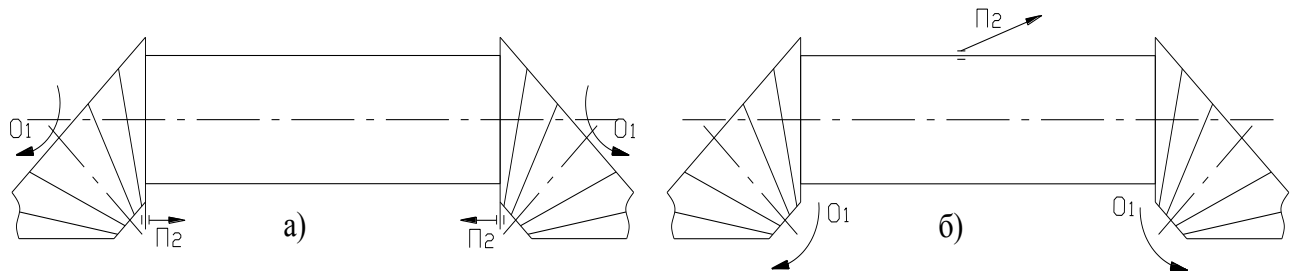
Схема обробки торців конічними фрезами з рухомою (б) і нерухомою (а) заготовкою
